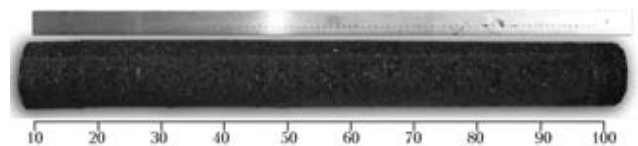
Заготовка, скомпактированная из стружки жаропрочного сплава ЭП609-Ш
